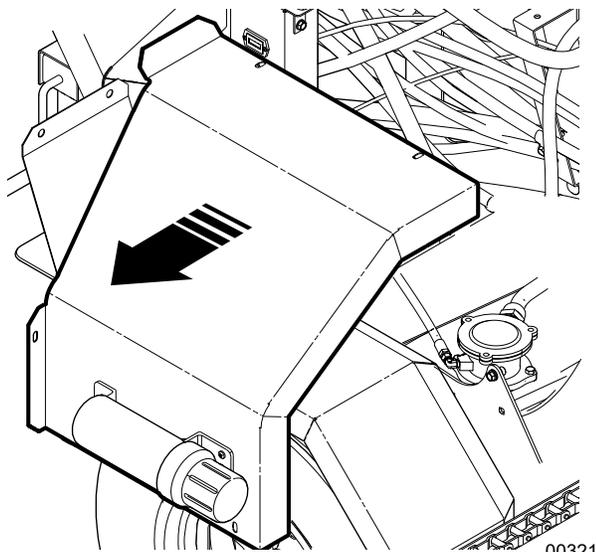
Couvercle du réservoir d'huile hydraulique
